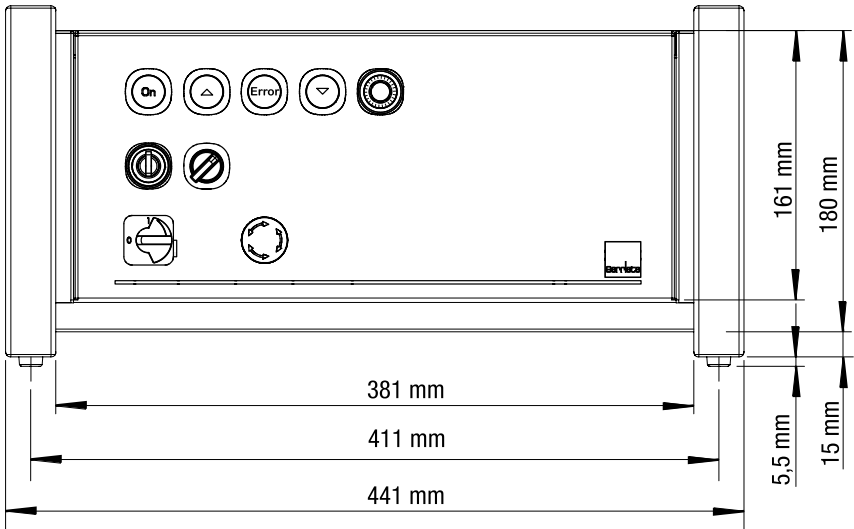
Frontansicht – Steuerung G-FRAME 54 (exemplarisch)
